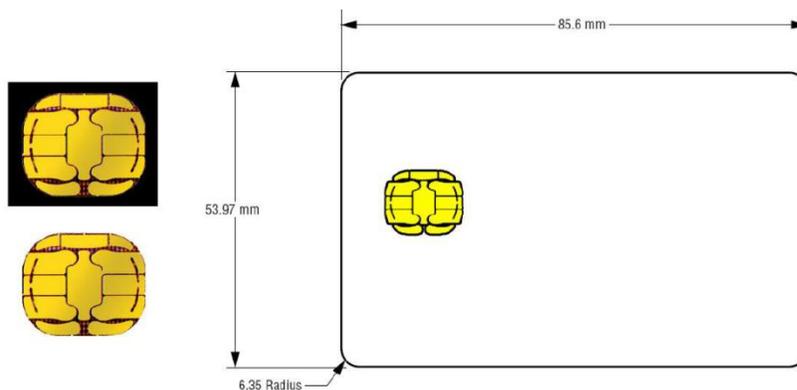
Dimensiones de la Tarjeta con Chip. Guía de Tecnología Chip de EMVCo (2015).
